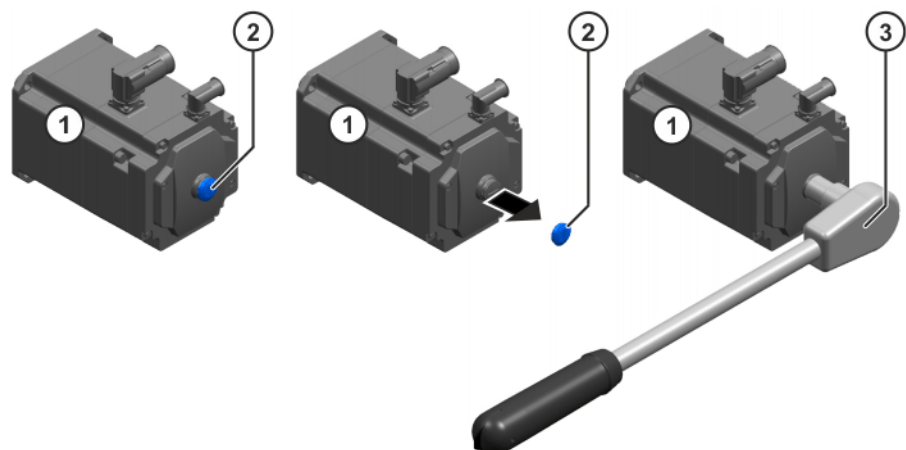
Montage du dispositif de dégagement sur le moteur
